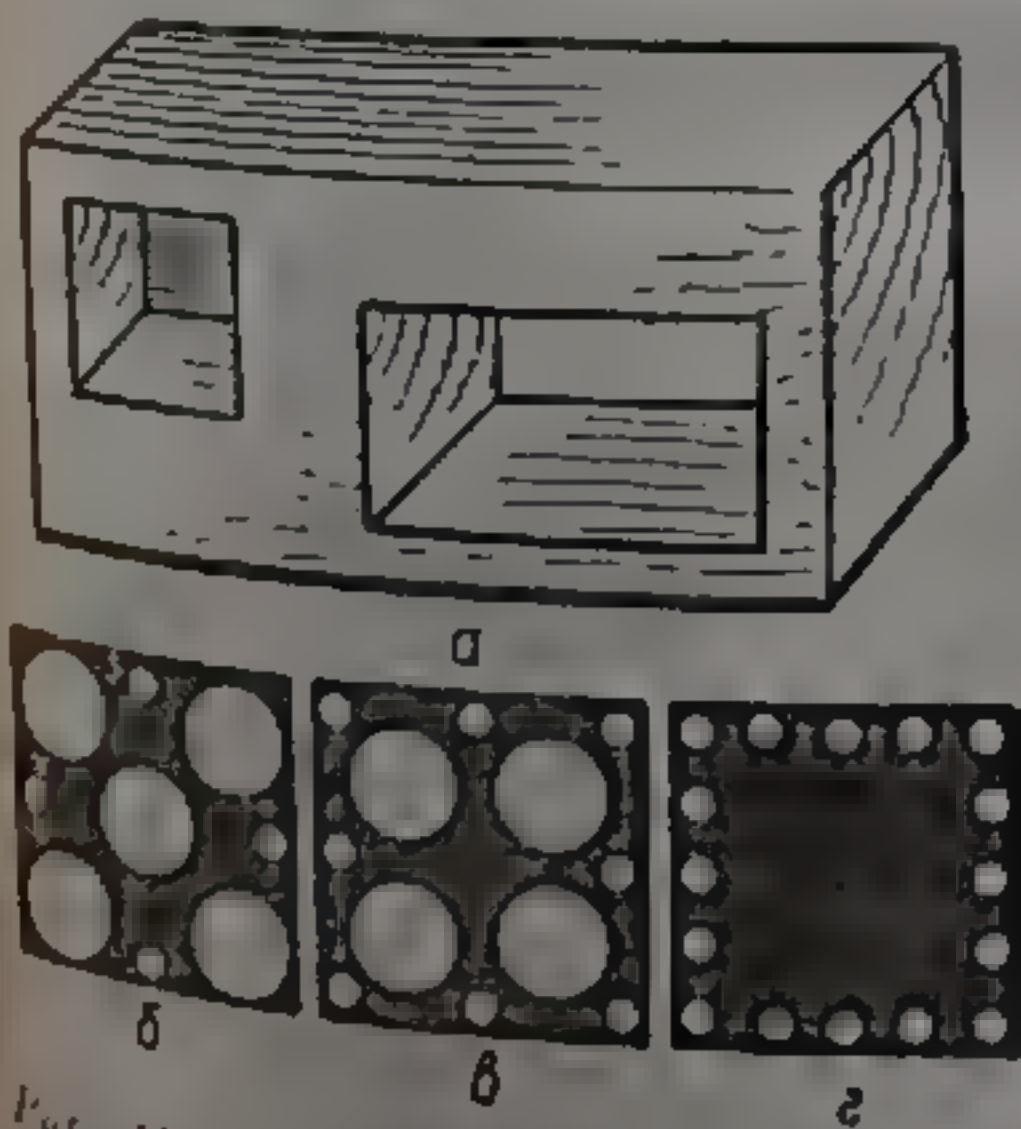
Выполнение глухого (сквозного) отверстия квадратной формы: а — общий вид; б—г — варианты сверления.
